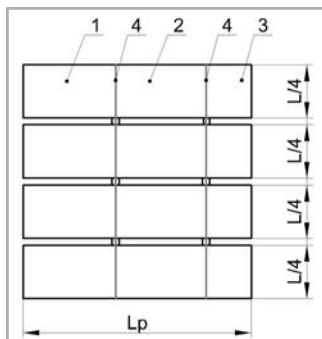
Схема одновременной сварки разверток дополнительных царг удлиненных обечайек: 1, 2 и 3 – листы разверток царг; 4 – соединительная планка; 5 – сварной шов; L – длина обечайки;  $L_p$  – длина развертки царги
